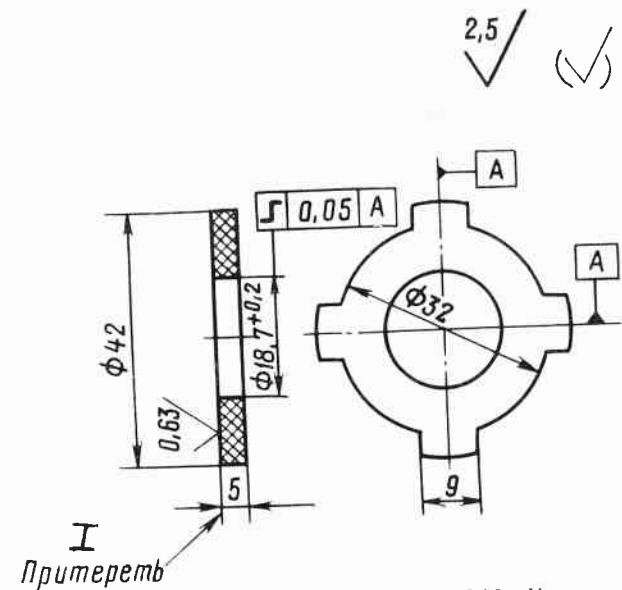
Корпус сальника — 5П12—37.12.03—11
